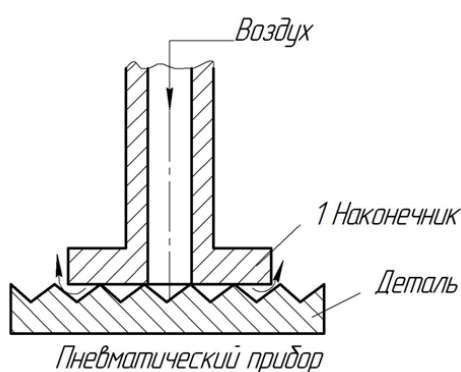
Схема измерения шероховатости пневматическим прибором
